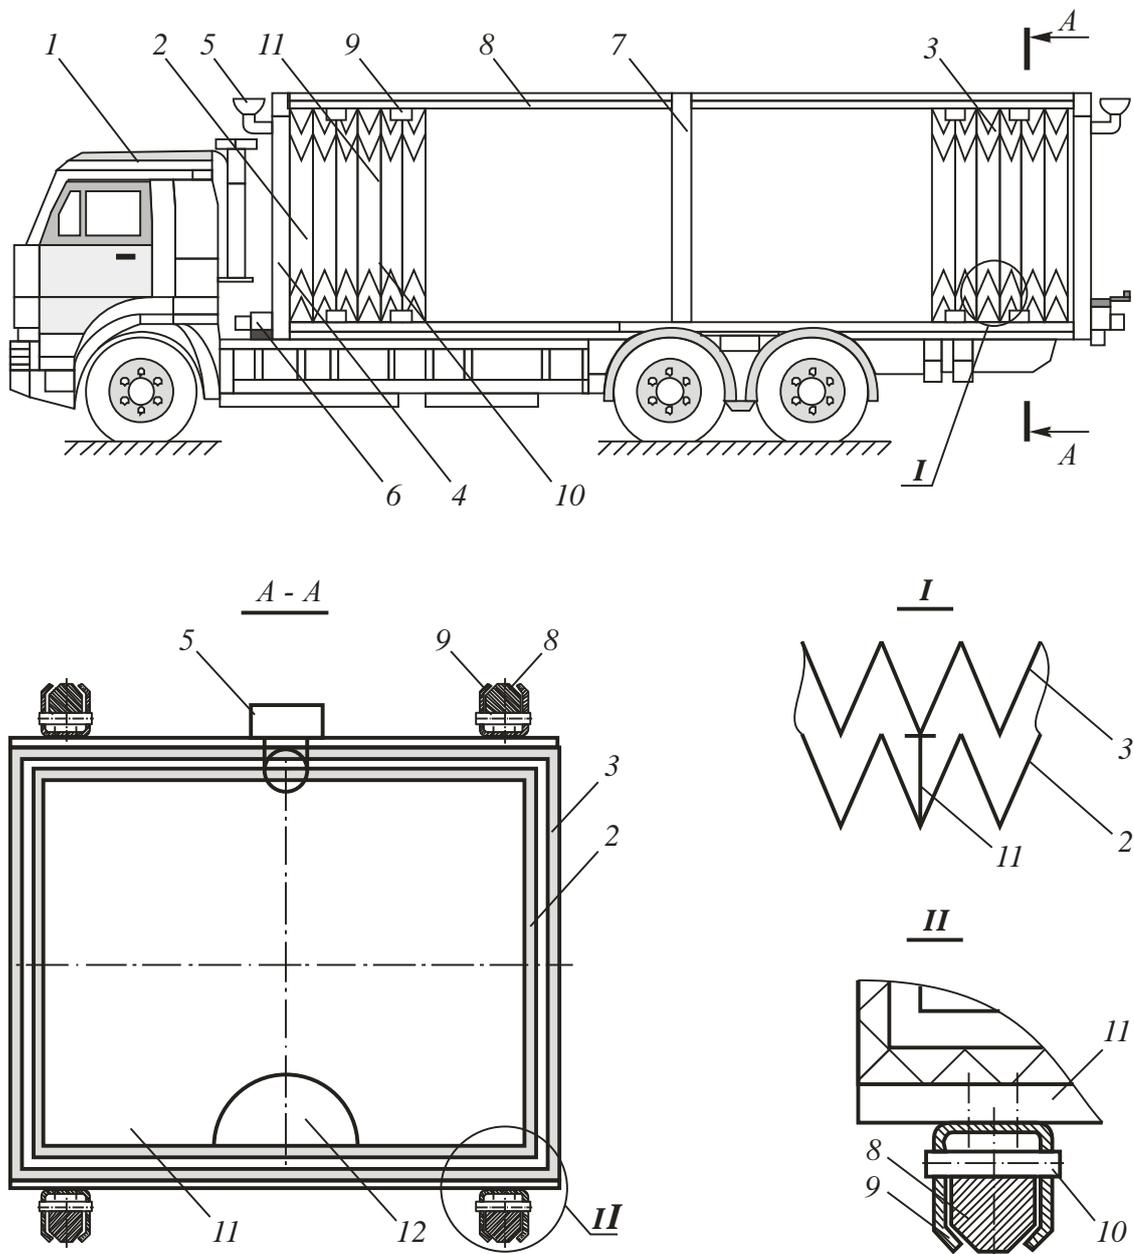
Транспортное средство в сборе: 1 – грузовой автомобиль; 2 – гофрированные резервуары; 3 – защита теплоизоляционная; 4 – баки; 5 – заливные горловины; 6 – сливные краны; 7 – металлическая арка; 8 – направляющая; 9 – держатель; 10 – ролик; 11 – поперечные волнорезы; 12 – отверстия; 13 – ограничители.
